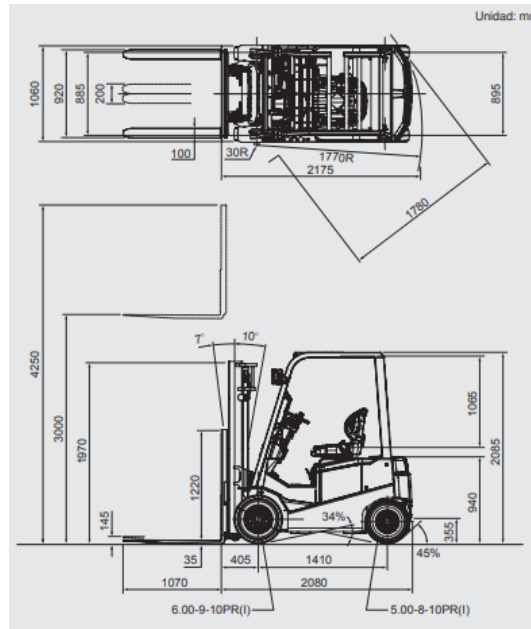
Dimensiones de un montacargas estándar de la marca TOYOTA [34].
